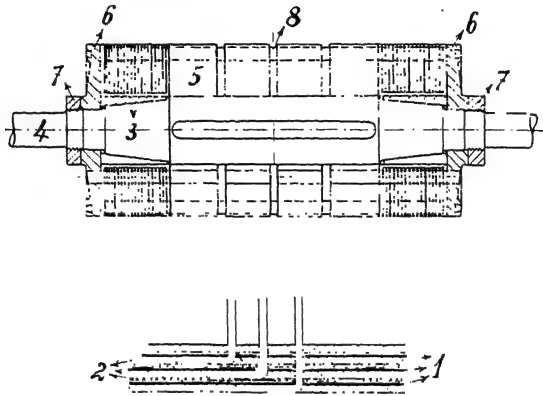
Siehe auch E. P. 13051 (Jahr 1904).
